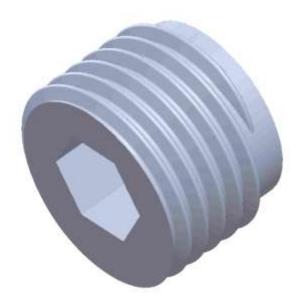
Bouchon fileté 6 pans creux dessiné par SolidWorks®
